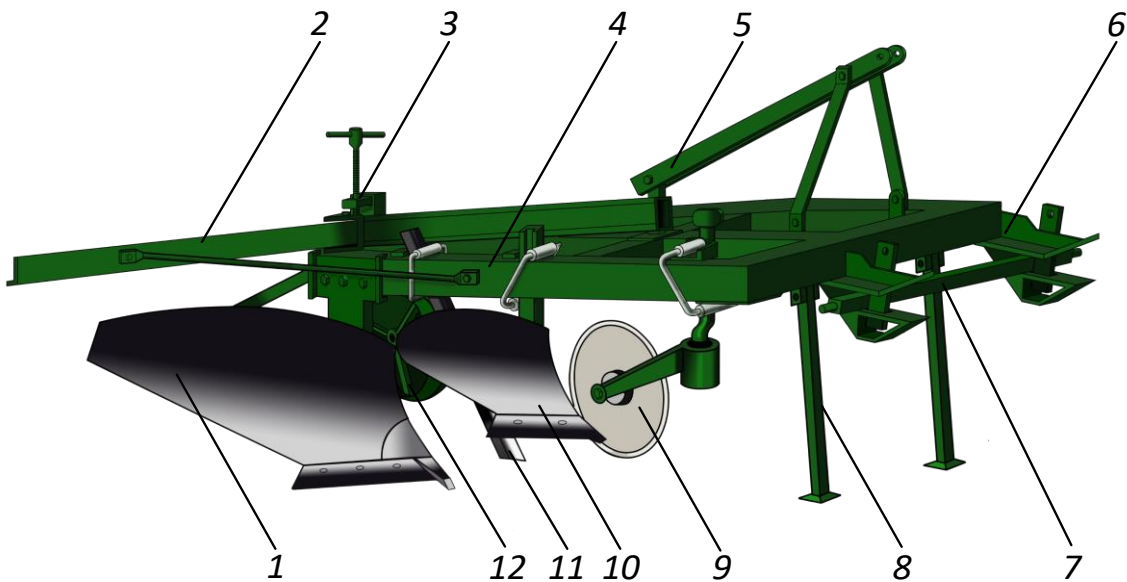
Плуг плантажний начіпний ППН-40: 1 – корпус; 2 – пристрій для навішування борін; 3 – гвинтовий механізм опорного колеса; 4 – рама; 5 – підвіска; 6 – вилка; 7 – вісь; 8 – підніжка; 9 – дисковий ніж; 10 – передплужник; 11 – чересловий ніж; 12 – опорне колесо
